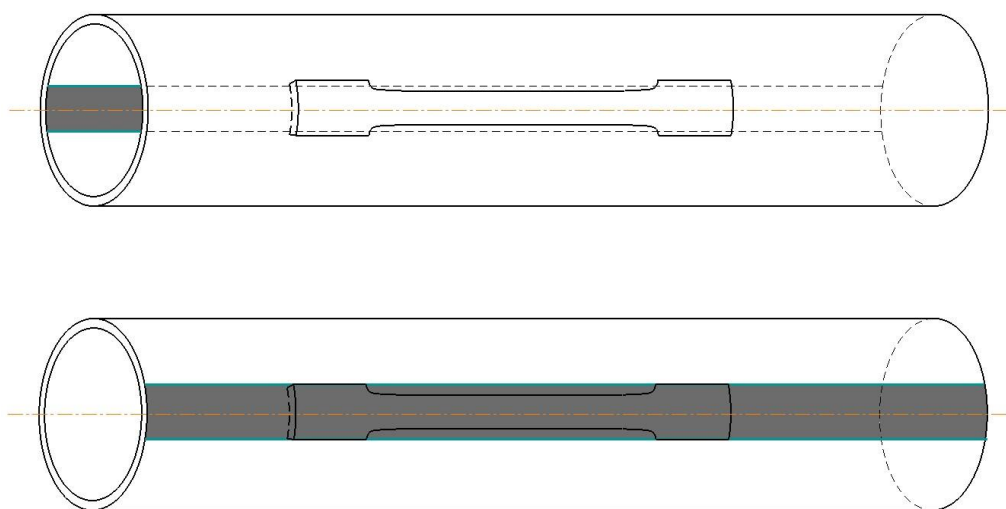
Схема вырезки образцов из трубы (по основному металлу и по металлу шва)
